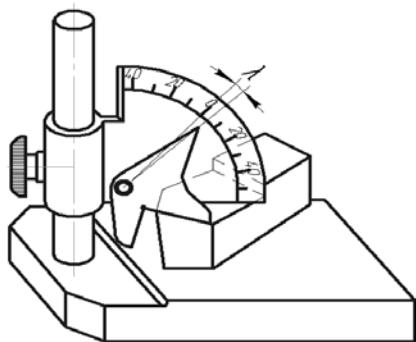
Вимірювання кута λ токарного прохідного різця
